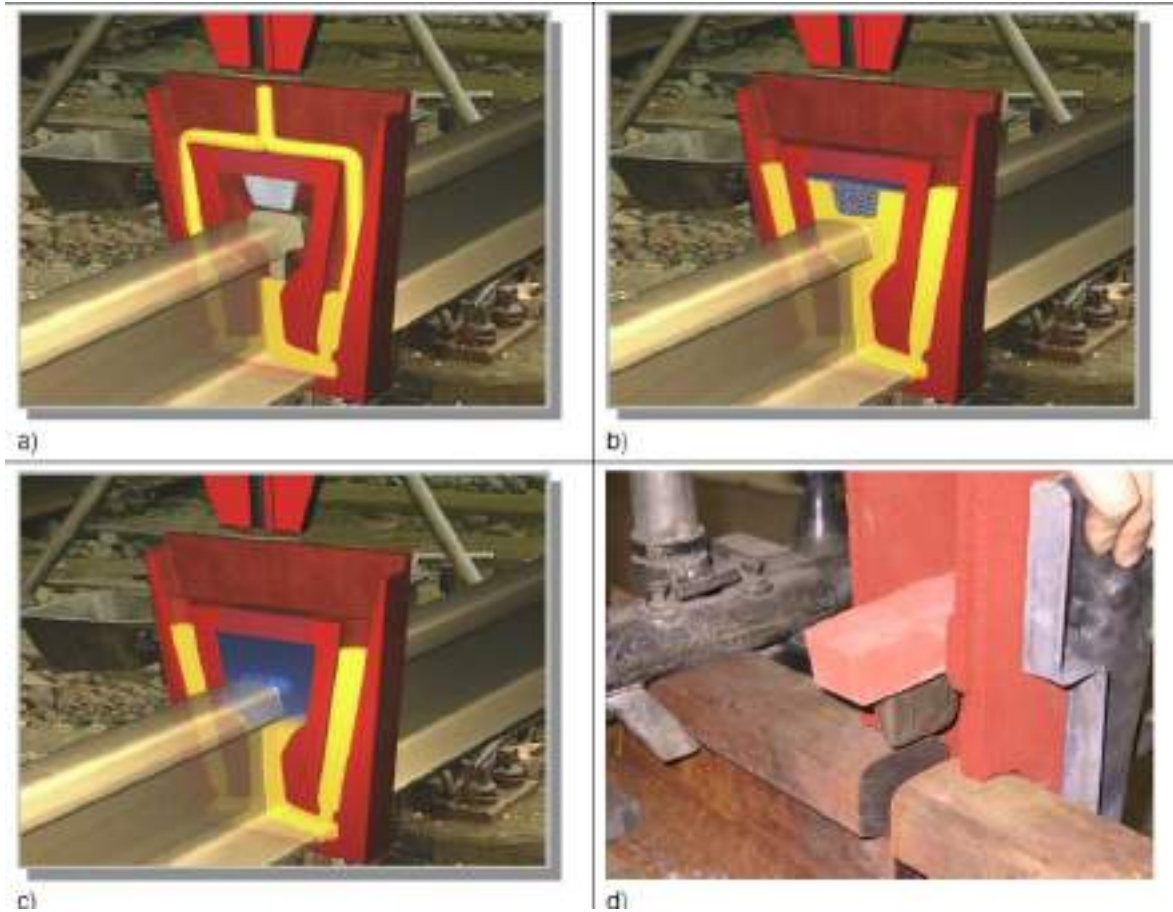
Схема термітного зварювання залізничних рейок [77]
